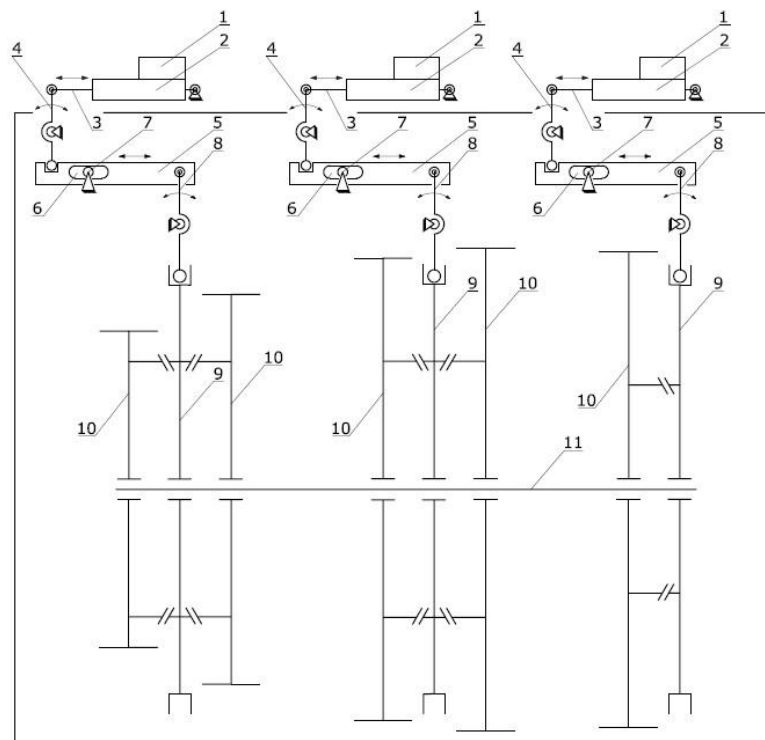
Кинематическая схема коробки передач с механизмами автоматического переключения передач.
